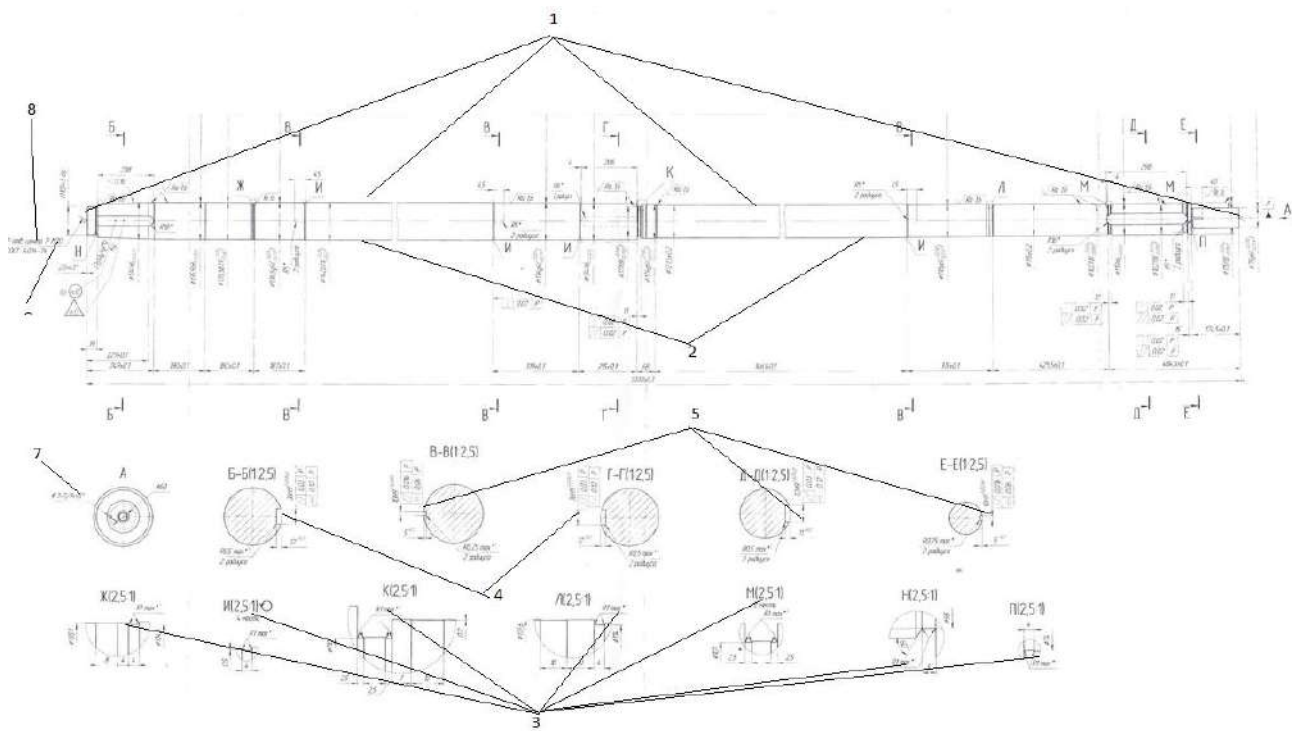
Обозначение обрабатываемых поверхностей на конструкторском чертеже
